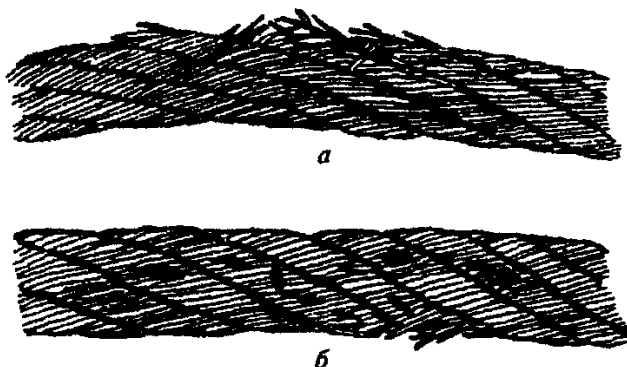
Обрывы и смещения проволок каната крестовой свивки
